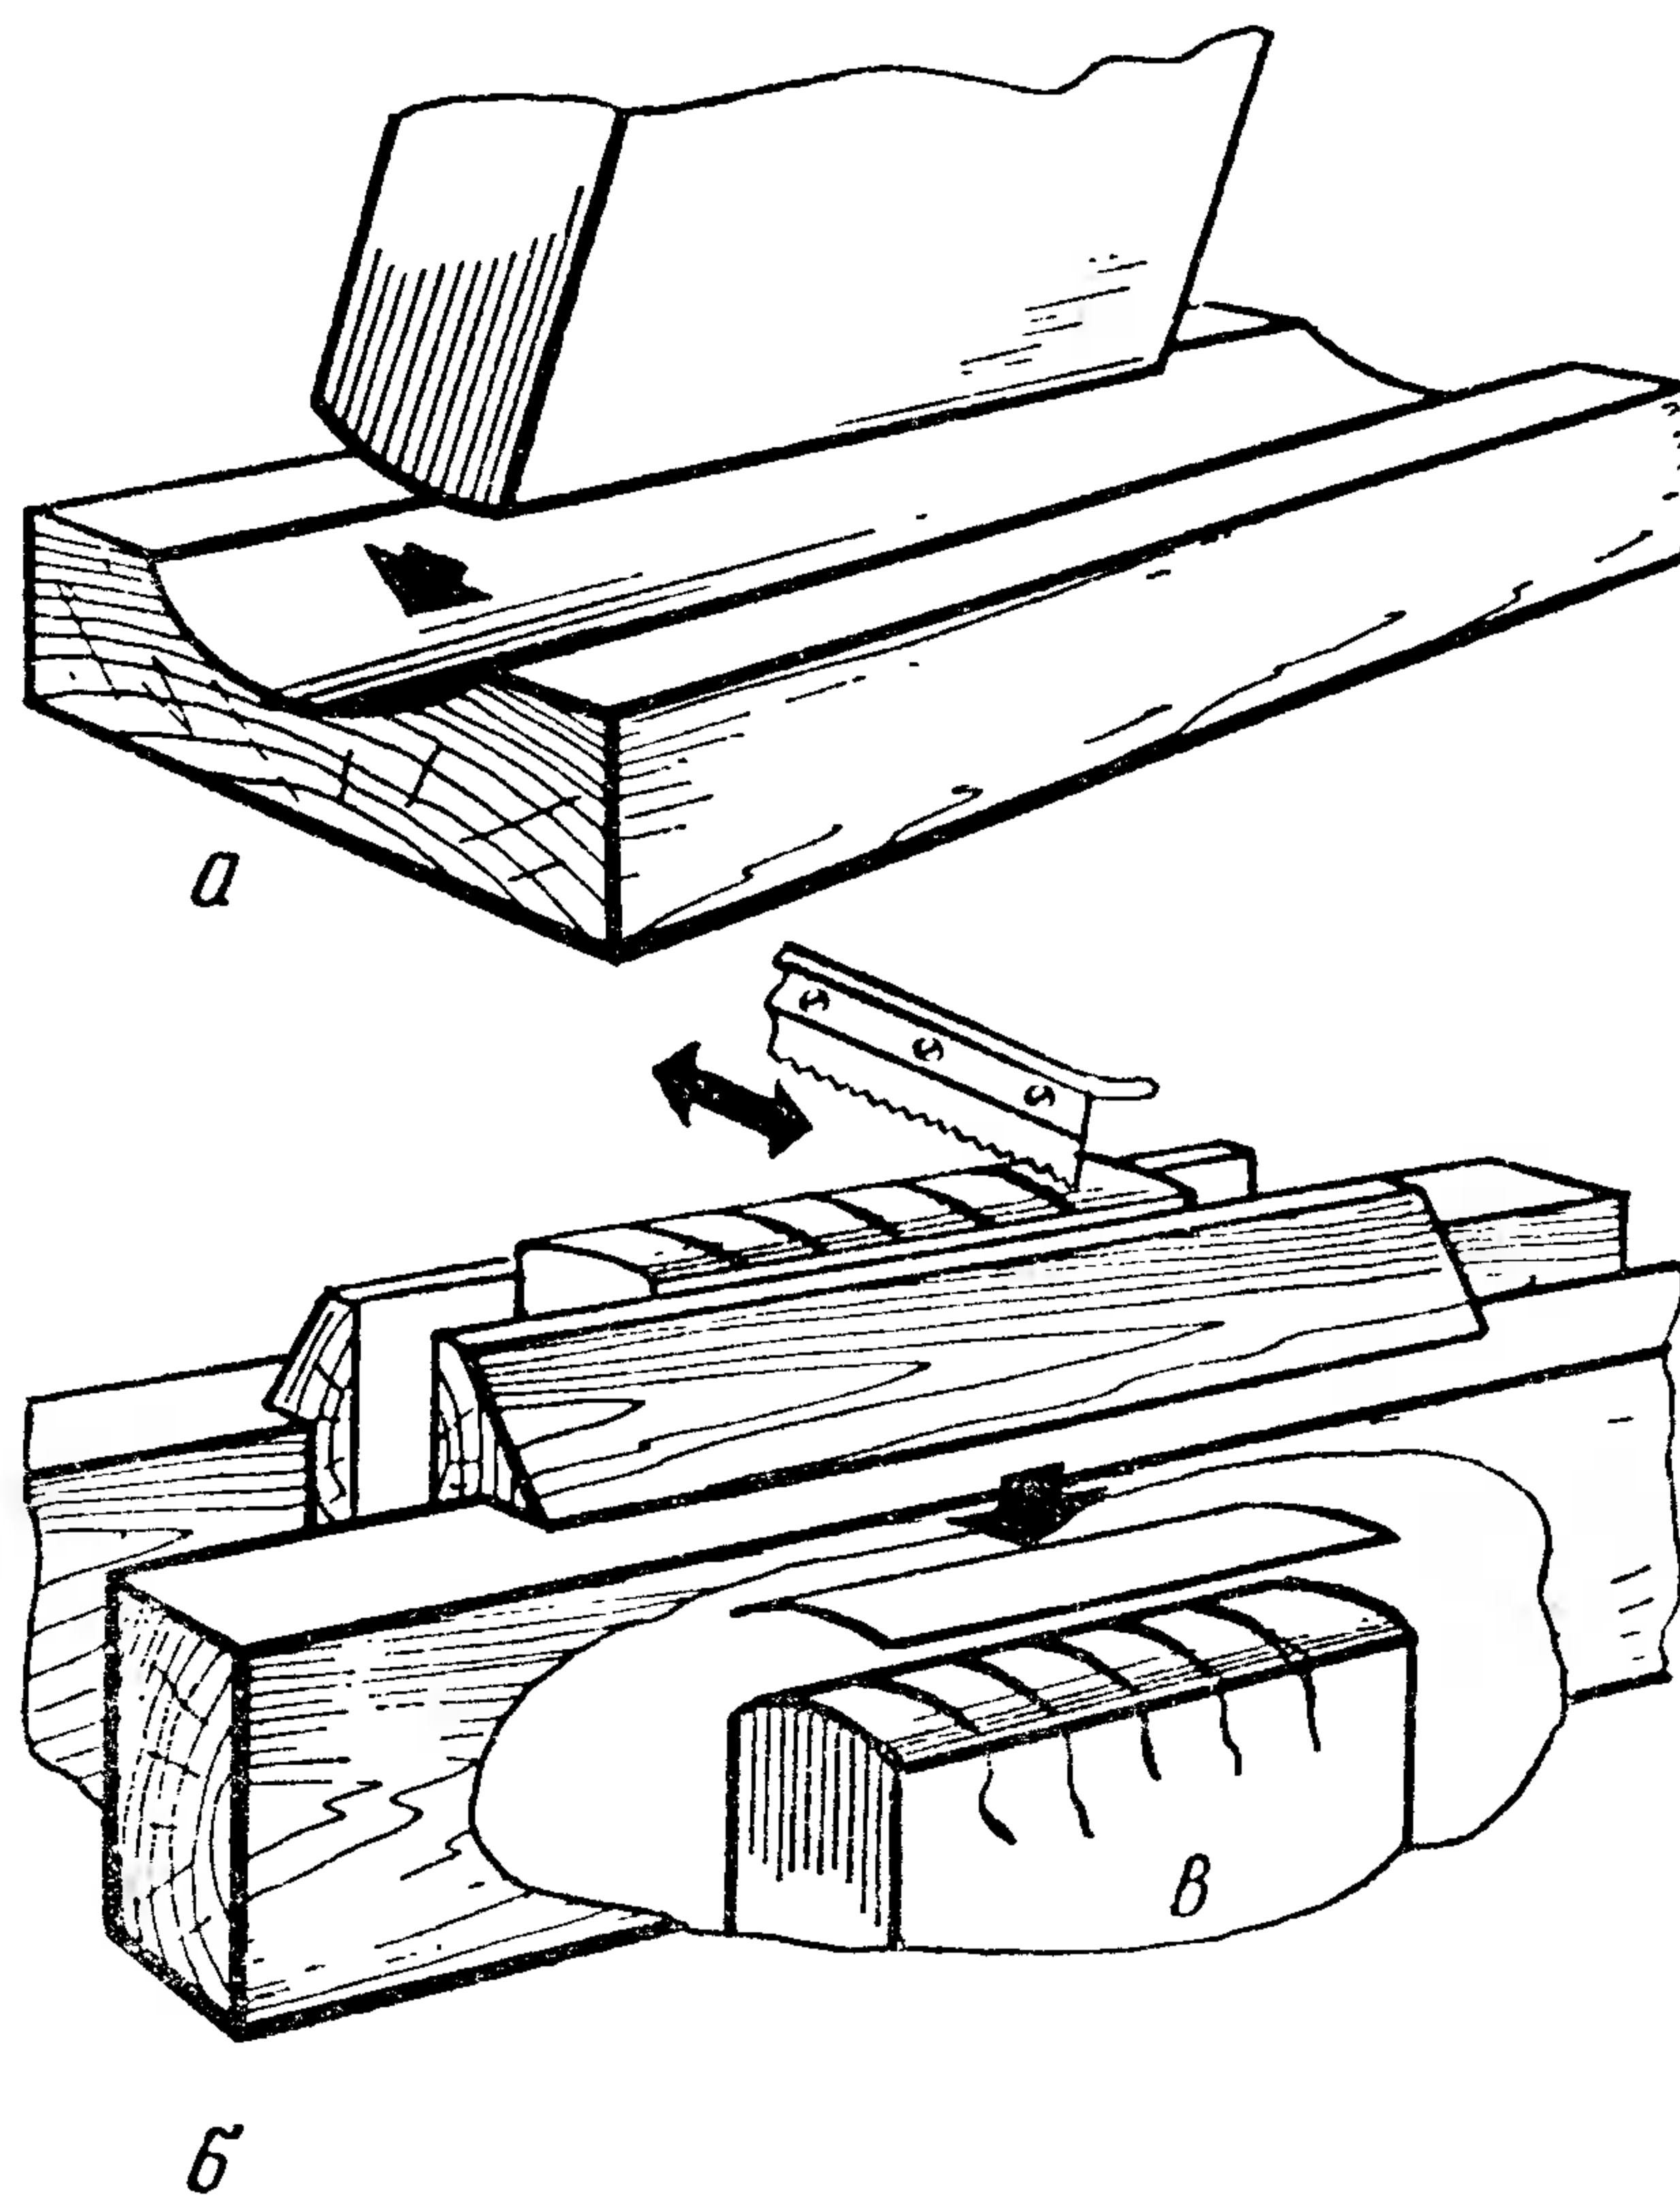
Обработка корешков книжного блока при бесшвейном скреплении: а — закругление; б — пропилка; в — прокладка упрочняющих нитей и обклейка.
